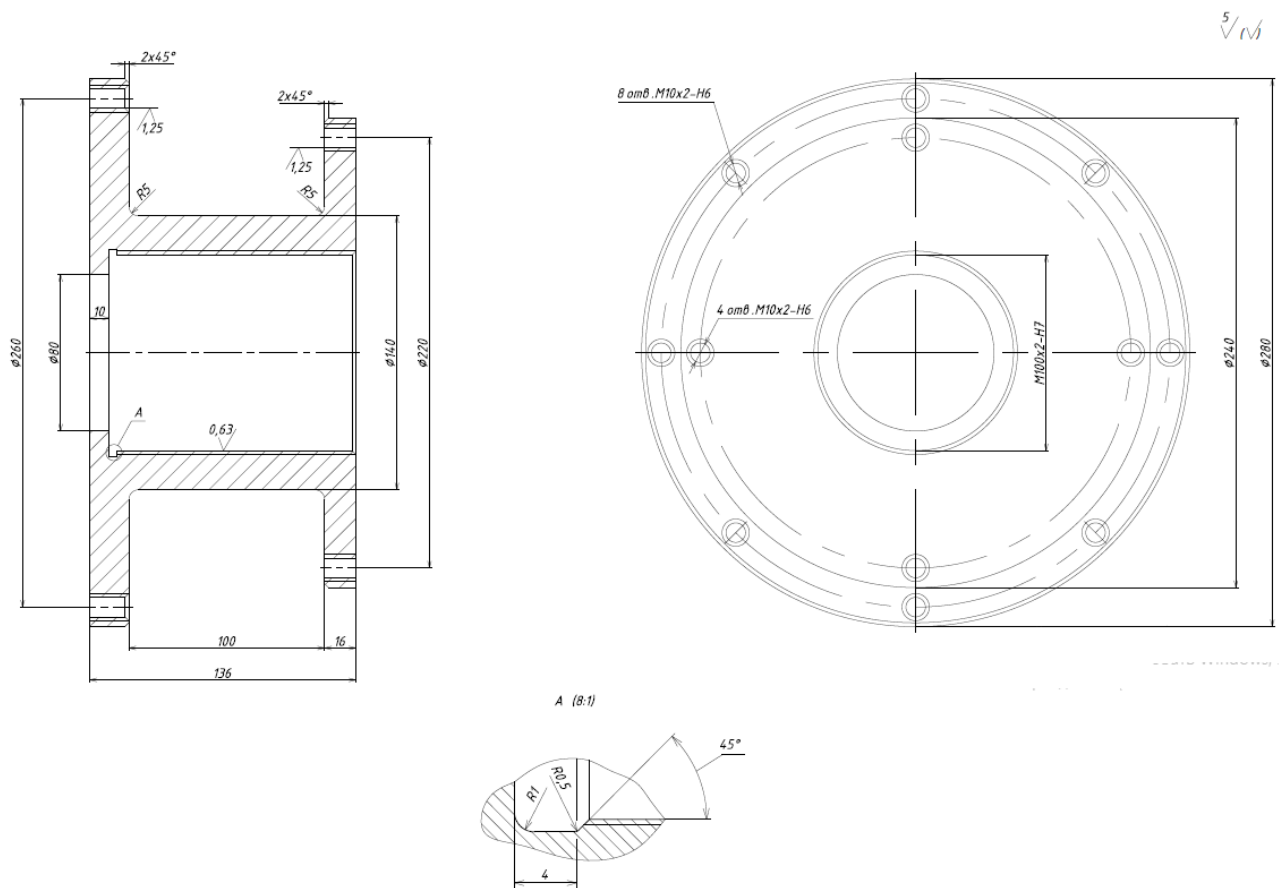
Ескіз деталі «Корпус підшипника»
